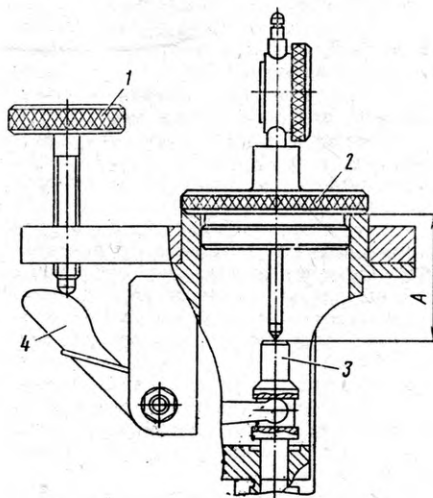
Настройка прибора ПР.722 индикаторным приспособлением:
